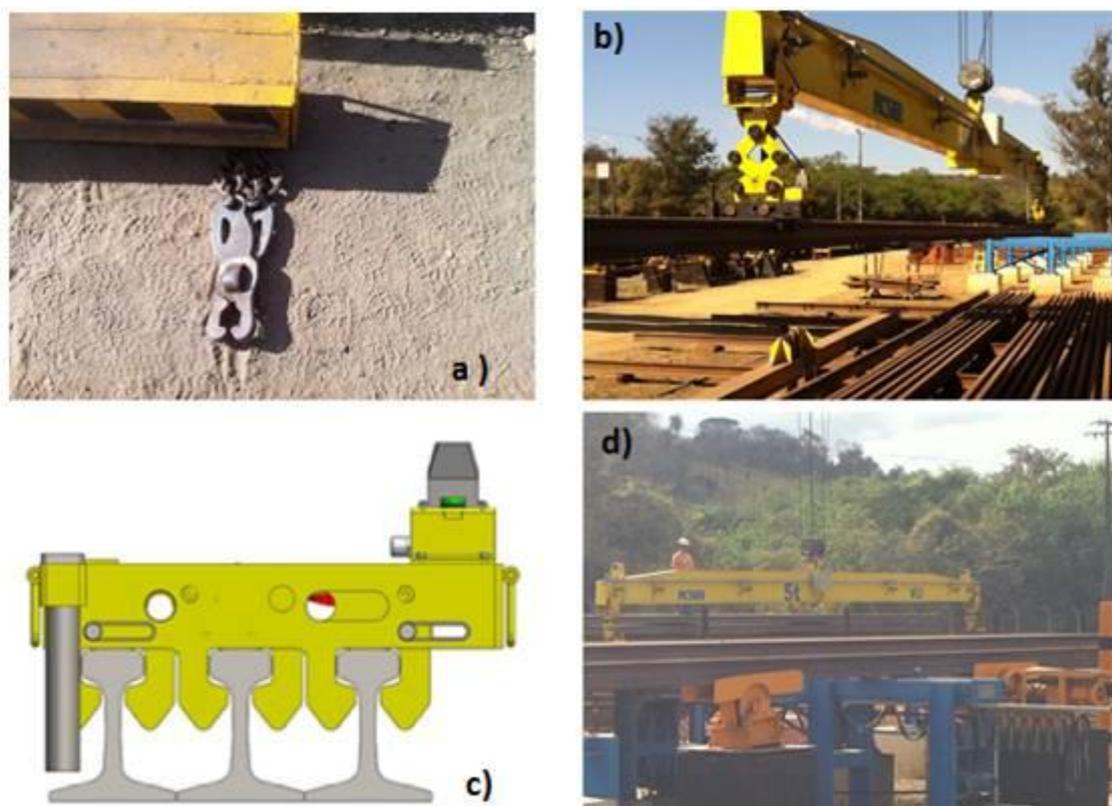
Viga Balancim. a) Detalhe do travamento manual da barra de carga. b) Viga Balancim em operação. c) Detalhe construtivo da Viga-Balancim. d) Operador e Viga Balancim
